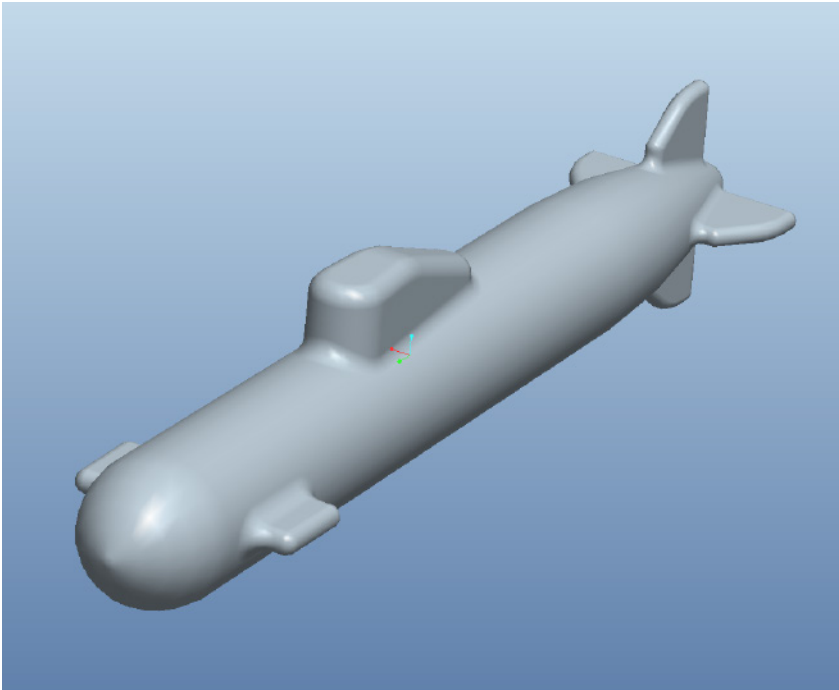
Geometrie des U-Bootes in Pro/ENGINEER
